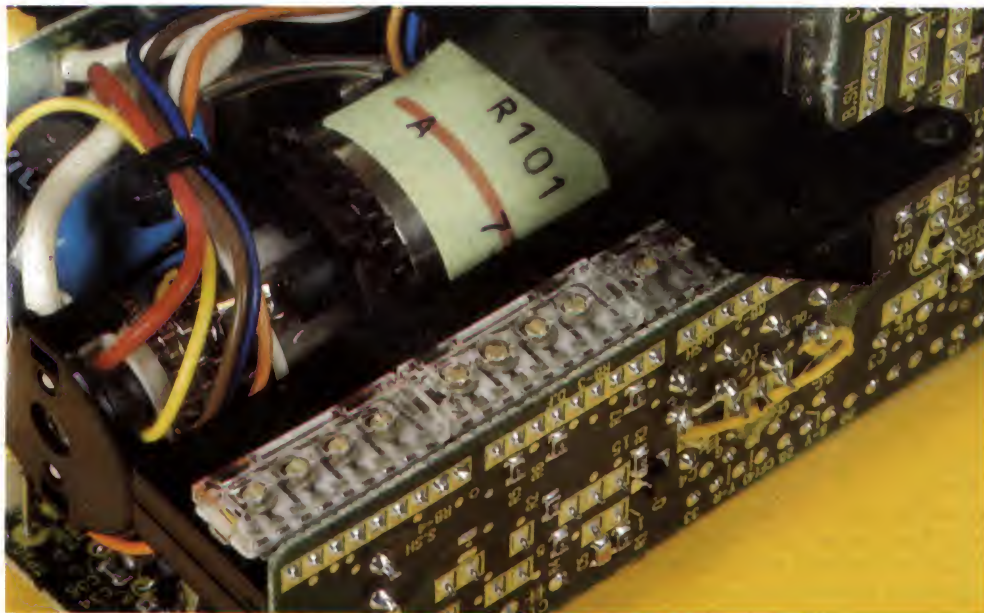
Vue intérieure de la caméra : le tube de prise de vue. Remarquez aussi les composants montés en surface.
